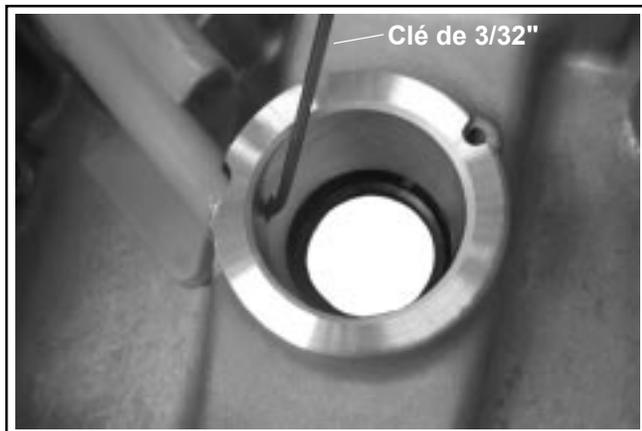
Contrôle de l'ouverture du passage du joint extérieur (style ouvert).
